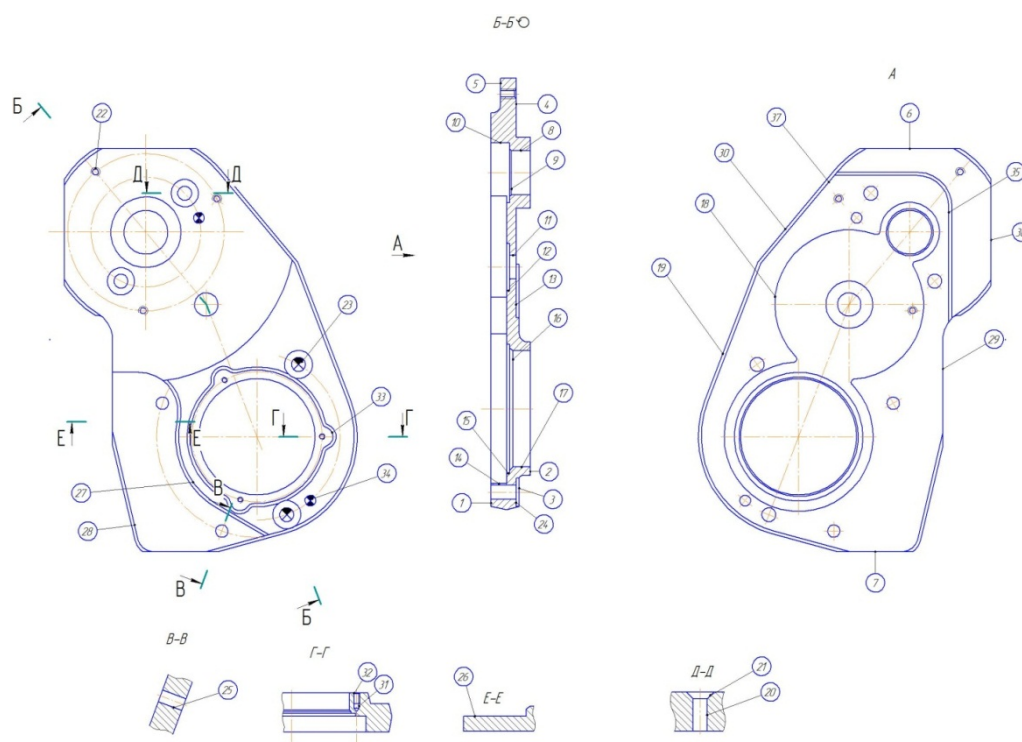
Эскиз детали с номерами обрабатываемых поверхностей
